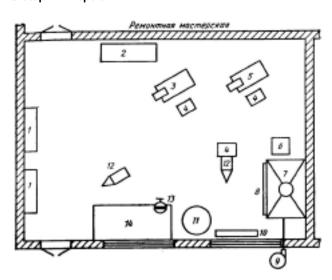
Размещение оборудования в кузнице II типа: 1— шкафы для инструмента; 2— место для заготовок и готовых изделий; 3— пневматический молот; 4— столики для инструмента; 5— пневматический молот; 6— ящик с углем; 7— одно огневой металлический горн; 8— вешалка для инструмента; 9— вентилятор; 10— скамейка; 11— бачок с водой; 12— наковальни; 13— стуловые тиски; 14— слесарный верстак
